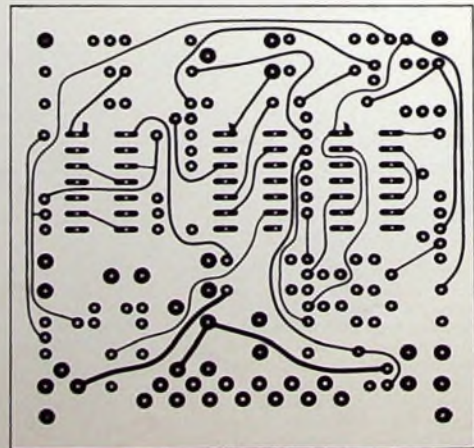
Printplatte (Bestückungsseite) im Maßstab 1:1
